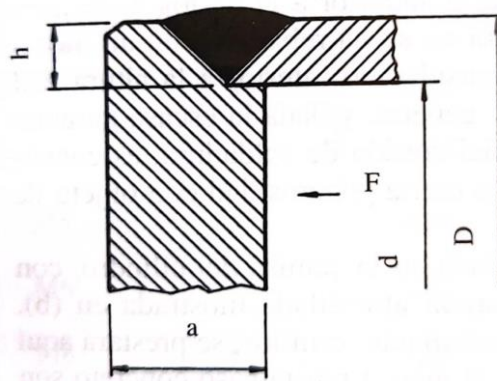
Fijación de la tapa por soldadura a tope en 45°
